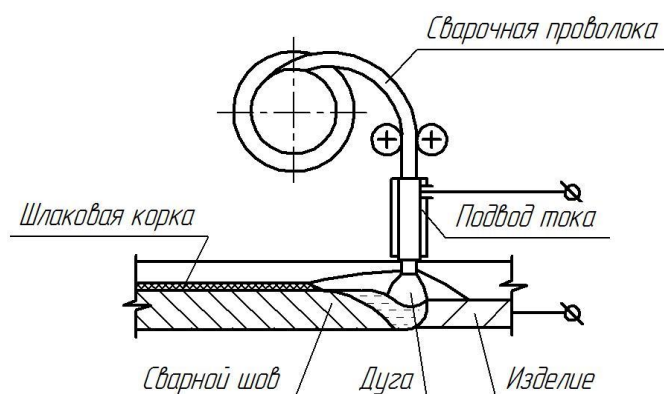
Схема сварки самозащитными порошковыми проволоками
